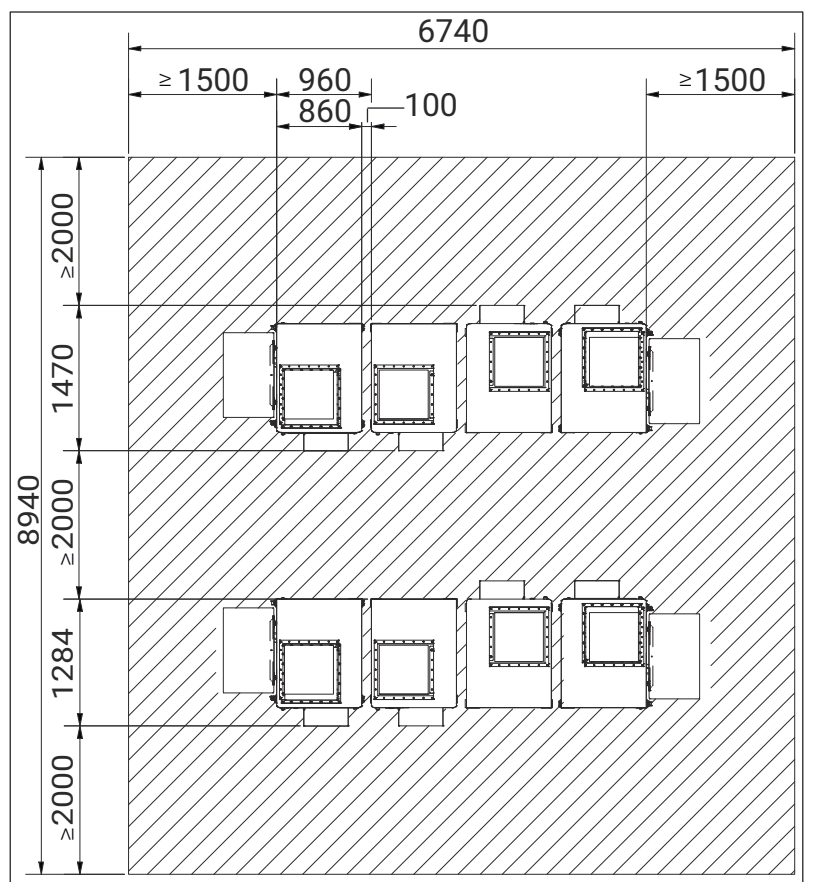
Installationsfläche [mm] Mehrfachsystem Variante 2
